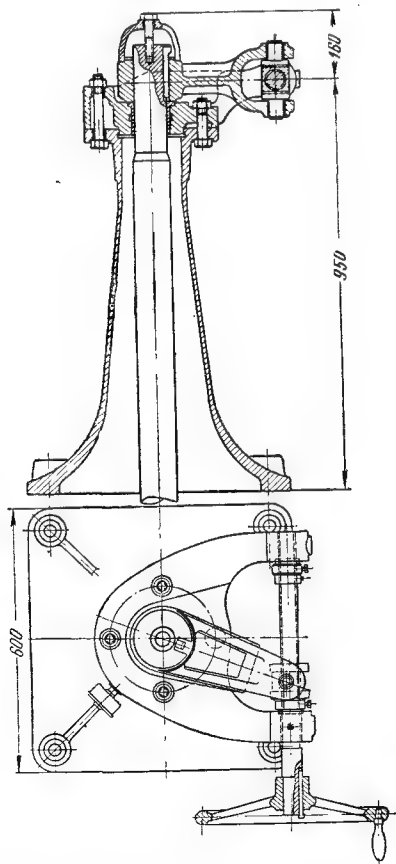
Ручной механизм для поворота вертикального регулирующего вала для турбин марок Р300.
